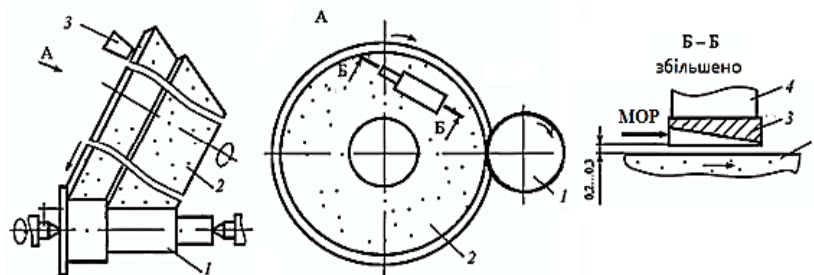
Схема УЗ техніки подачі МОР при суміщеному торці круглого шліфування: 1 - заготовка; 2 - шліфувальний круг; 3 - насадка для подачі МОР; 4 - перетворювач УЗК
